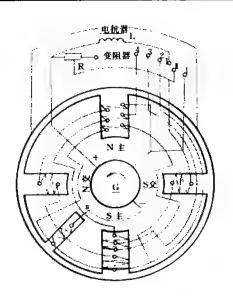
AX1-165 型直流焊接发电机电气线路图
